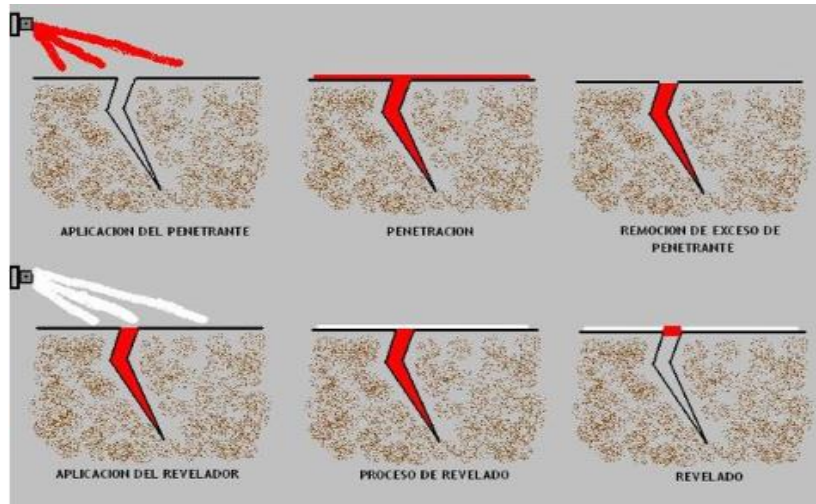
Inspección por líquidos penetrantes Fuente: (tallerjbordagaray, 2017).
